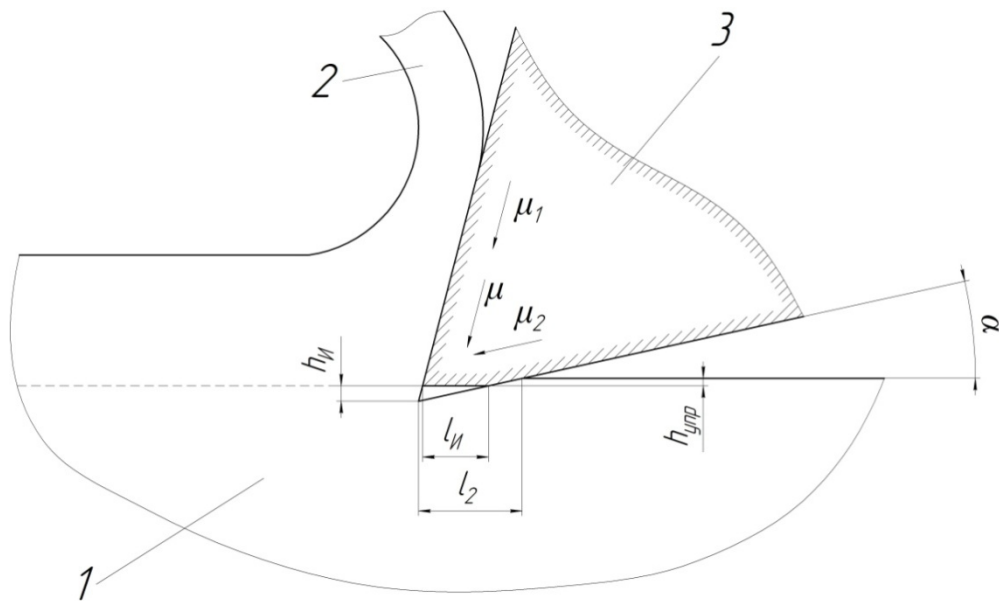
Схема контакта инструмента с заготовкой [135, 136]:
